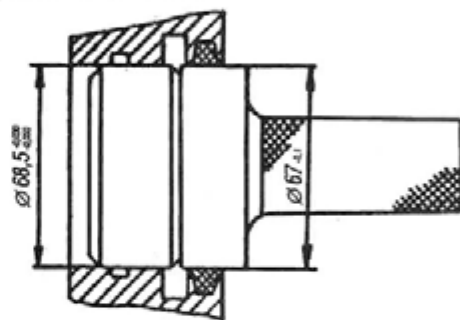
Оправка 5-У-27678 для обжима набивки заднего уплотнения коленчатого вала
